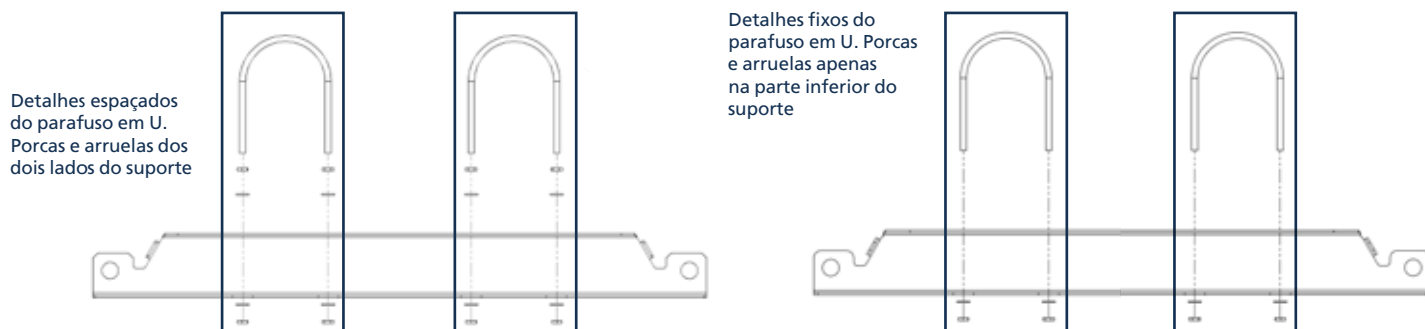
Suportes de suspensão do aquecedor U-Bolt a U-Tube
